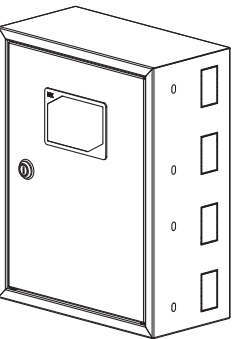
Общий вид корпуса ЯУР-380-300
